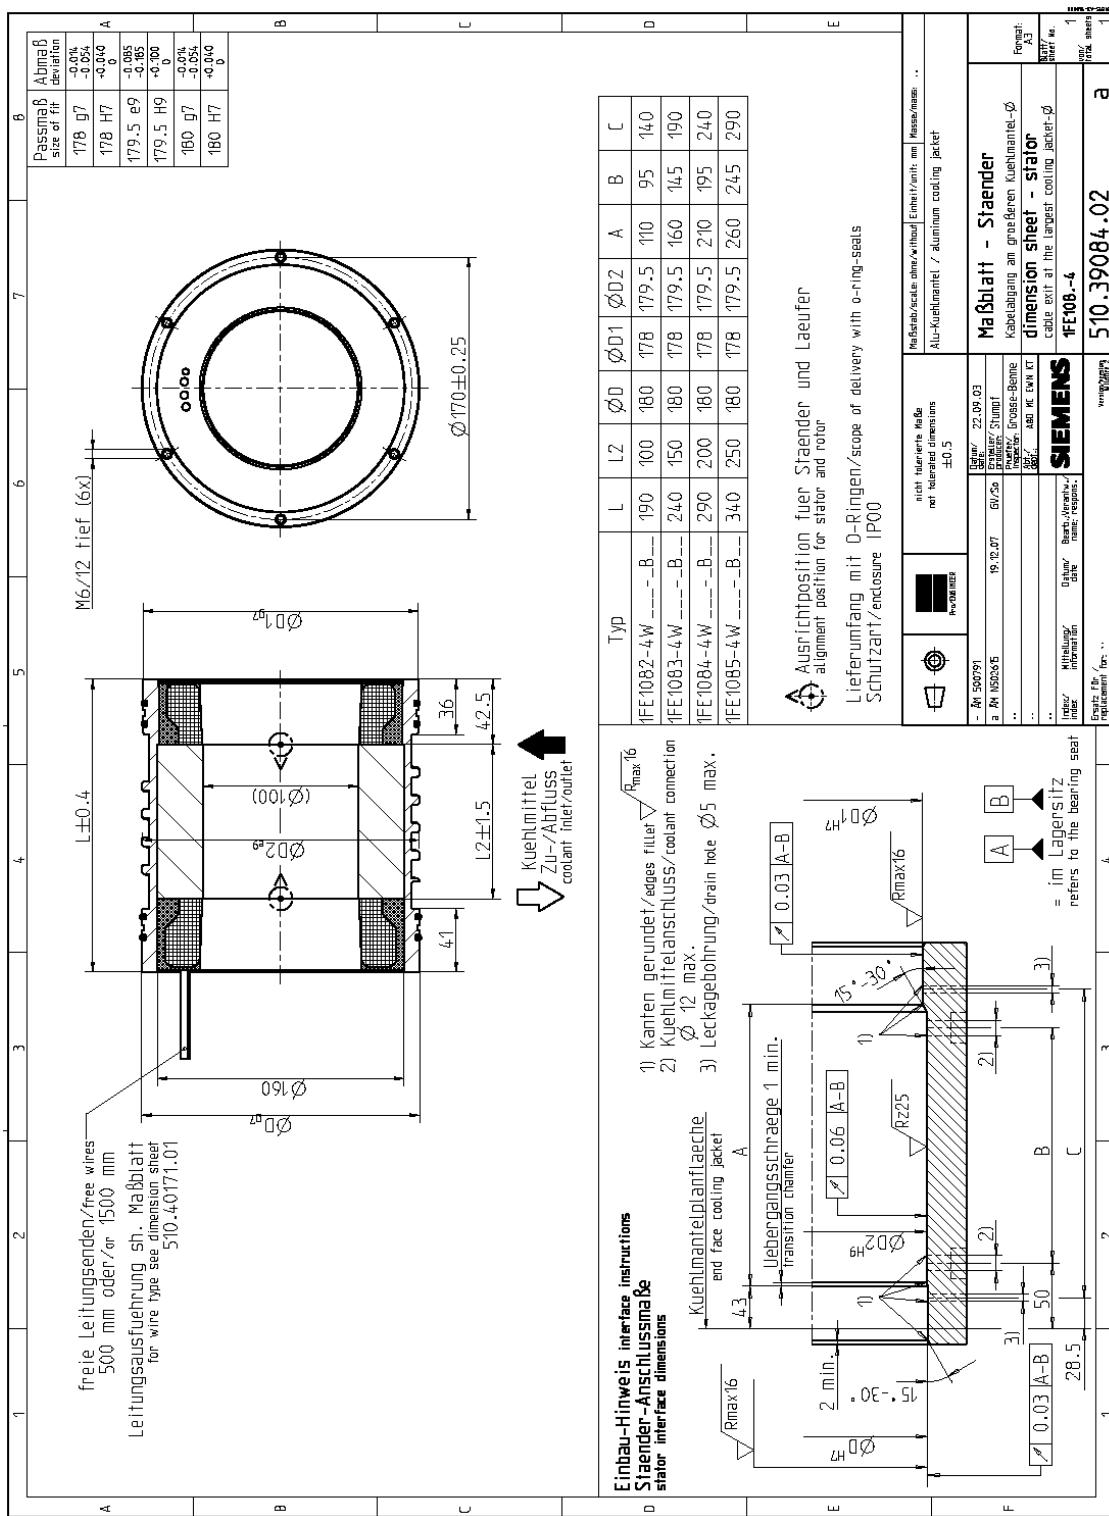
1FE108□-4, Ständer mit Kühlmantel, Kabelabgang am größeren Kühlmanteldurchmesser
